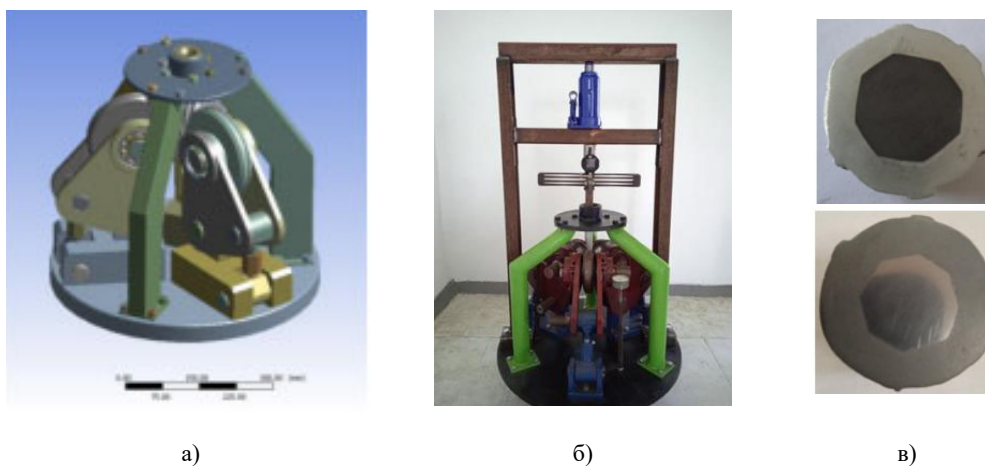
Трироликова волока для зовнішнього обтиснення циліндричної заготовки на профільній оправці неприводними роликами: а – CAD-модель; б – загальний вигляд експериментальної установки; в – отримані трубчасті деталі з полігональним профілем каналу [9]
